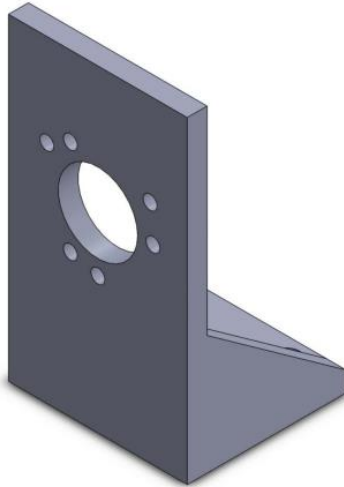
Diseño de base para sensor de posición LPD3806.
